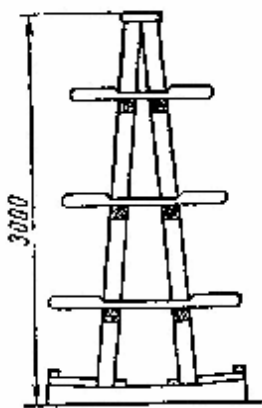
Пирамидальный стеллаж для вертикального хранения прутково-го материала
